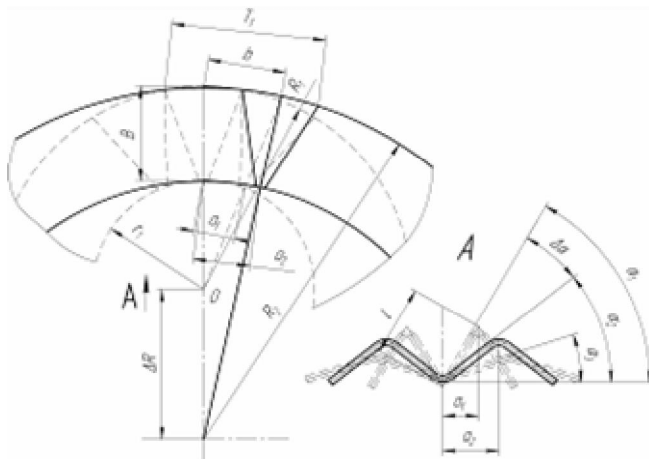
Розрахункова схема відпружинення профільної гвинтової заготовки
